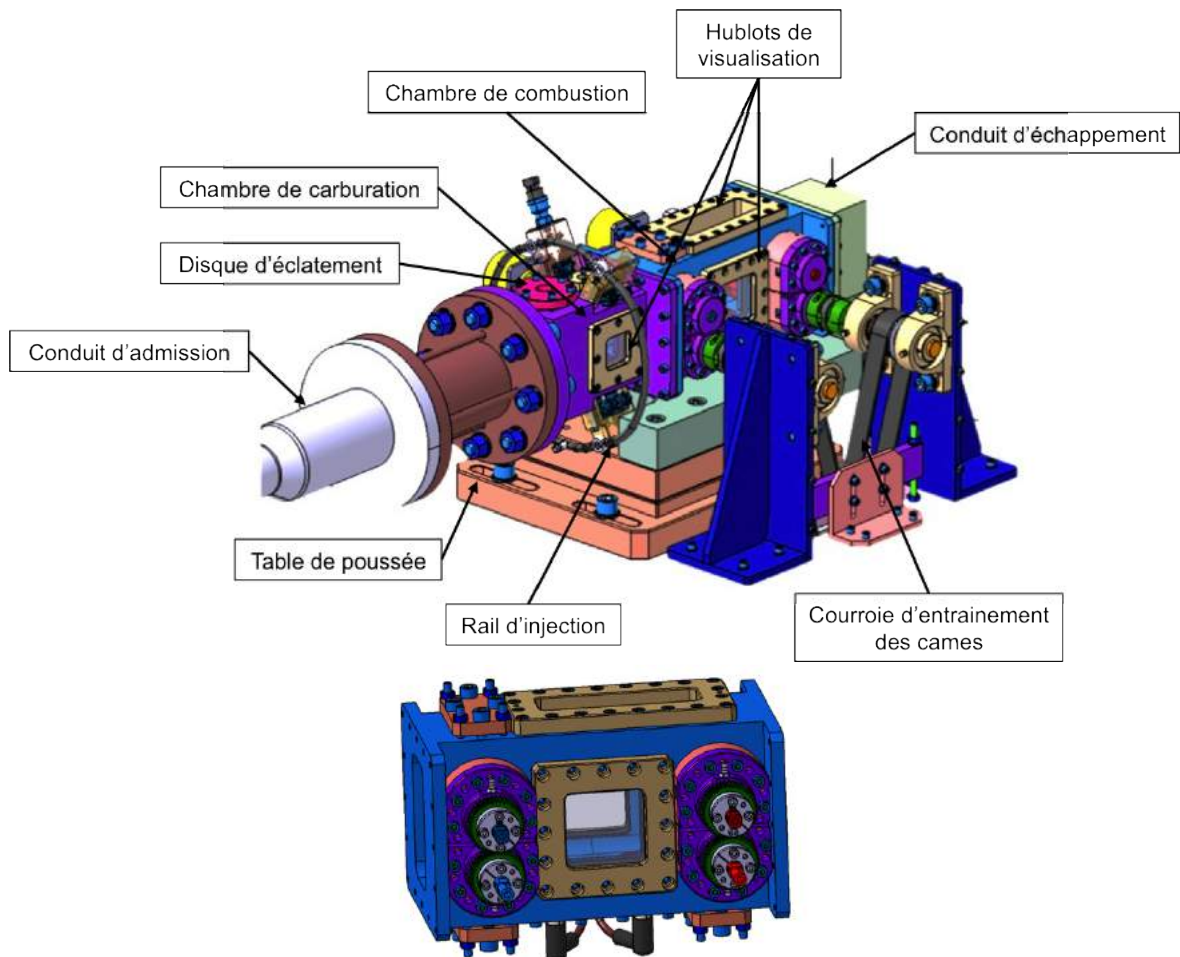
Vue CAO du banc d'essai. Haut : Vue globale. Bas : zoom sur la chambre de combustion.
